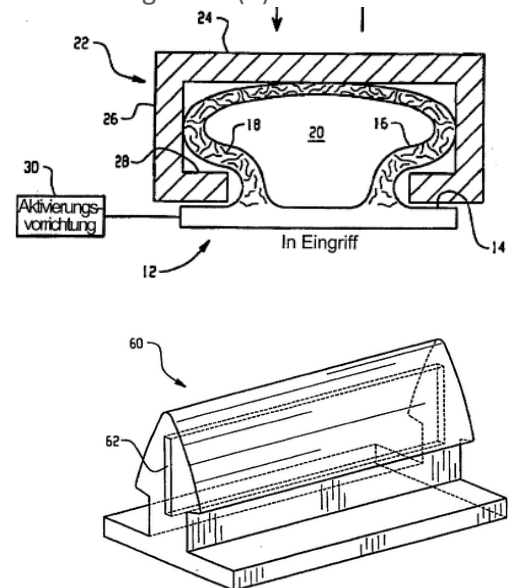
Reversible Befestigungsmechanismen; Querschnittsansicht in Eingriff (o), Vorsprung einer weiteren Ausführungsform (u)⁵⁰
